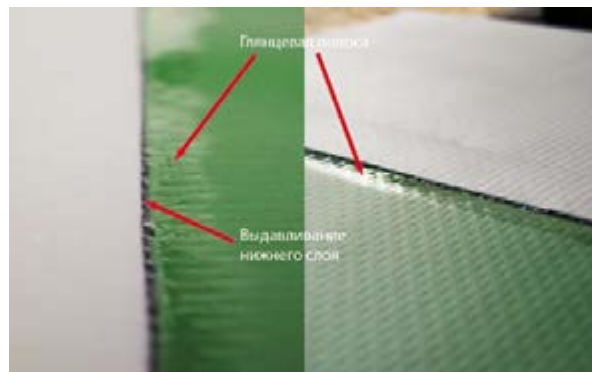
Визуальная проверка качества сварного шва
